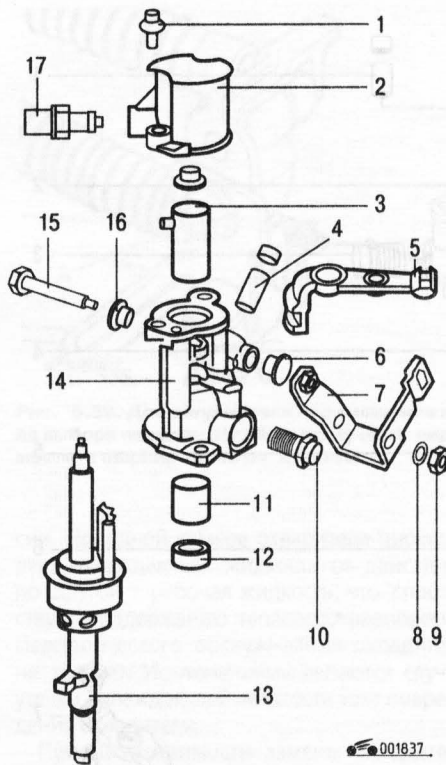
Механизм выбора передач: 1 – винт; 2 – крышка; 3, 4, 6, 16 – втулки; 5 – рычаг переключения передач; 7 – рычаг предварительного выбора передач; 8 – шайба; 9 – гайка; 10 – стопорный болт; 11 – опорная втулка; 12 – кольцо; 13 – вал механизма выбора передач; 14 – корпус; 15 – болт; 17 – выключатель фонарей заднего хода
